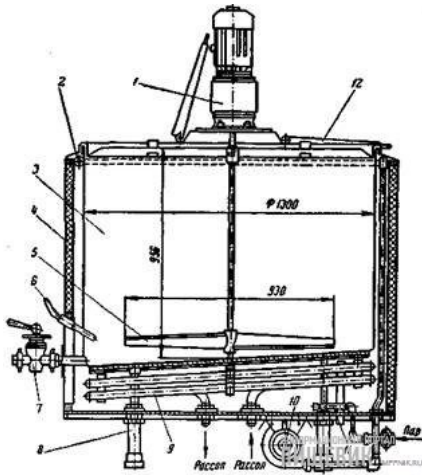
Танк вертикальный для кисломолочных продуктов: 1 — штуцер для трубопровода; 2 — вал мешалки; 3 — кольцевой ороситель; 4 — стальной кожух (рубашка); 5 — мешалка; 6 — внутренний резервуар; 7 — изоляция и облицовка; 8 — нижний
